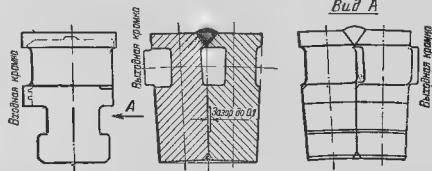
Сварной пакет из двух лопаток для первого венца турбины ВК-50-1 ЛМЗ.
